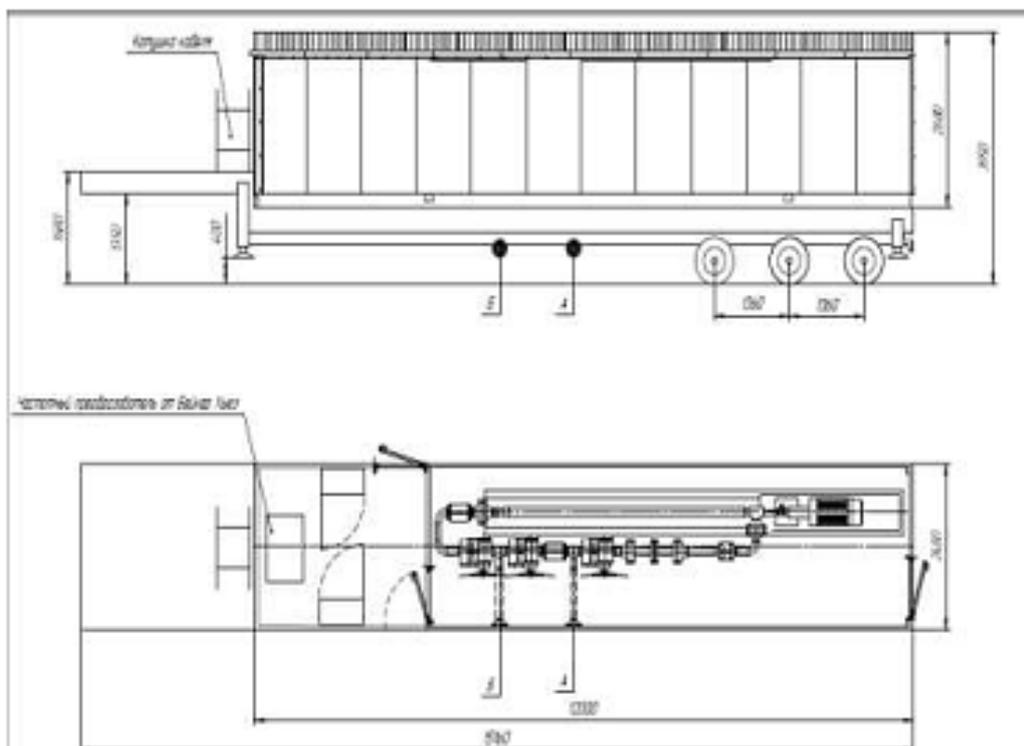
Общий вид автомобильного низкорамного прицепа для установки горизонтальной насосной установки
